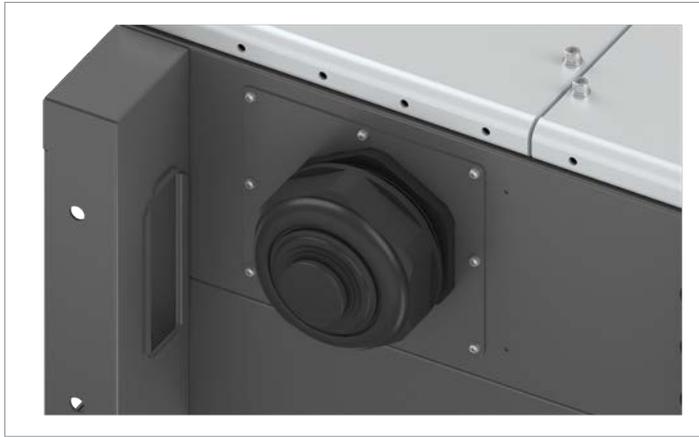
AC-Kabeldurchführung mit serienmäßiger AC-Kabelverschraubung
